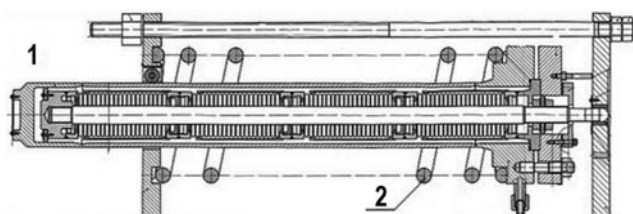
Фрагмент регулирующего устройства СПОТ: 1 – поршневой механизм пассивного привода; 2 – возвратная пружина
